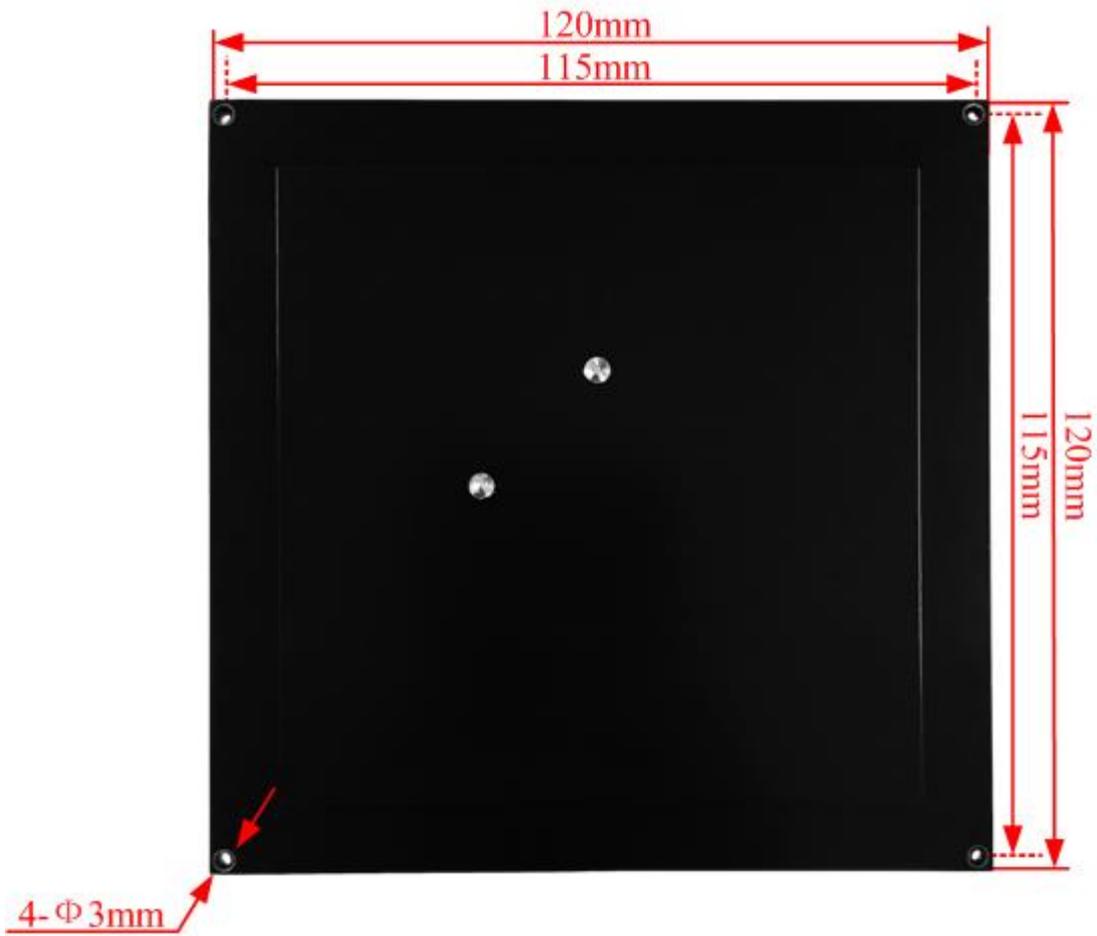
6dBi 板状 PCB 天线长宽、定位孔尺寸
